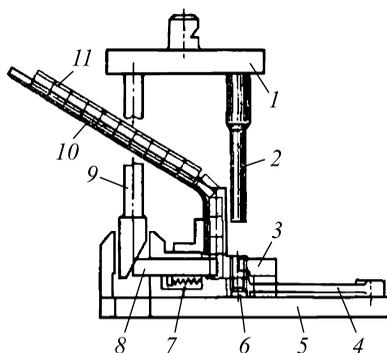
Автоматическое приспособление для запрессовки втулки в шатун автомобильного двигателя
